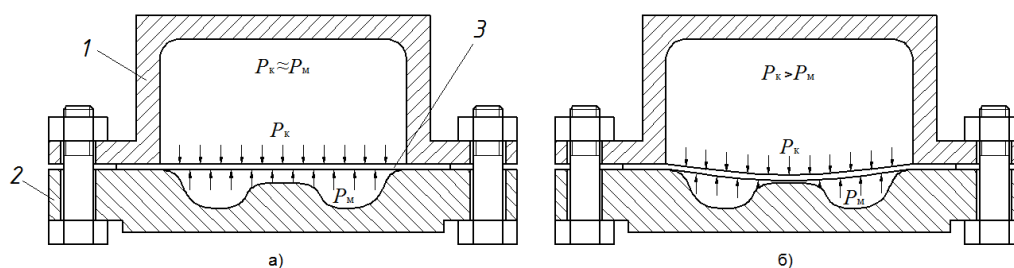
Схема газовой формовки с противодавлением. а) нагрев заготовки, $P_k \approx P_m$; б) деформирование заготовки, $P_k > P_m$; 1 – камера сгорания; 2 – матрица; 3 – заготовка
